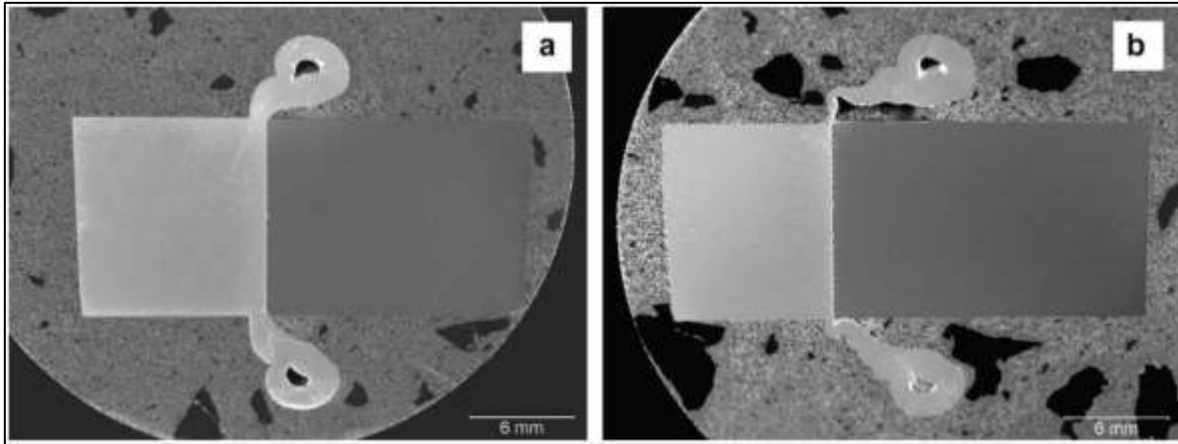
Macrografías de soldaduras disímiles de diseño de barra con barra [41]
